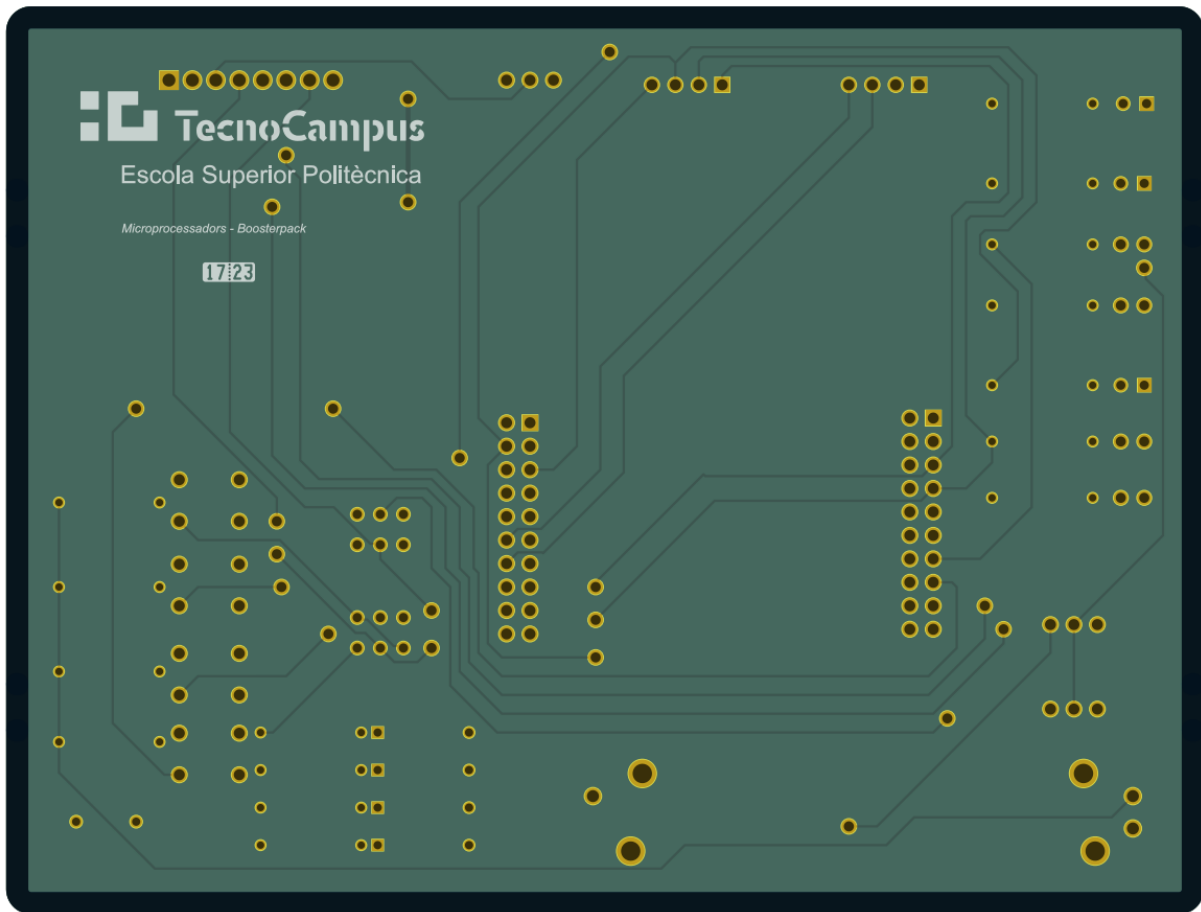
Confirmació del disseny de la PCB a fabricar, cara inferior.
